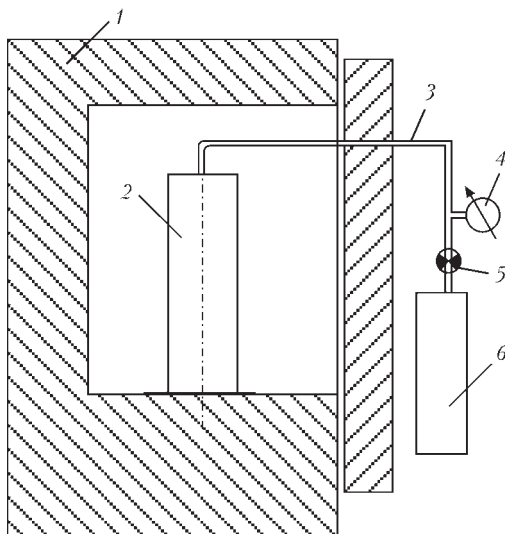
Схема проведения автономной вакуумной пайки: 1 — термическая печь; 2 — опытная заготовка; 3 — вакуумпровод; 4 — мановакуумметр; 5 — вентиль; 6 — форвакуумный насос
